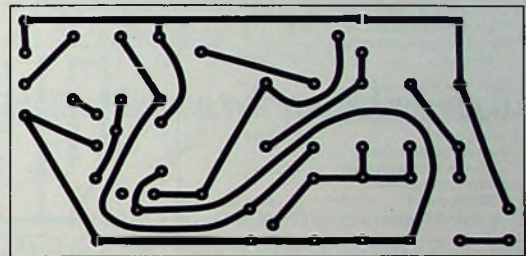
Printplatte für den elektronischen Drehzahlmesser (Maßstab 1:1)
